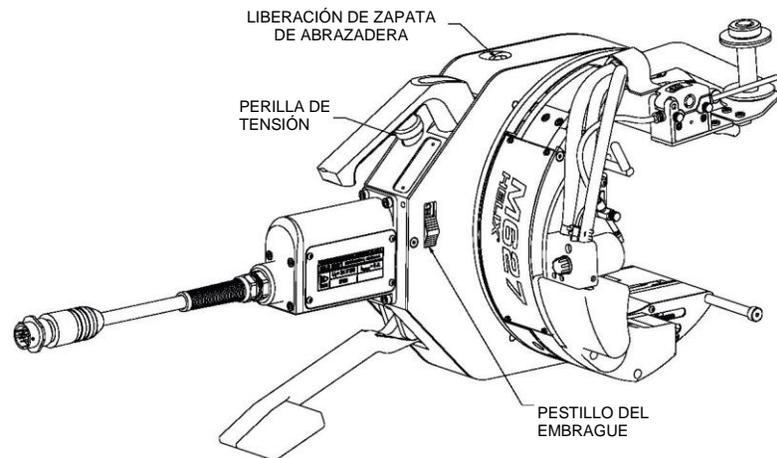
Componentes del cabezal de soldadura
